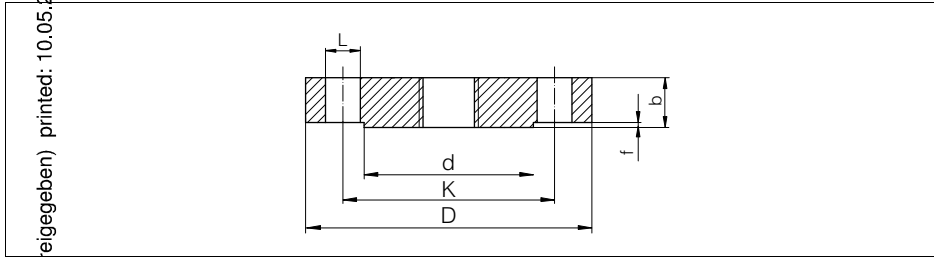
Maße - JIS-Flansch (Regular Flange)
